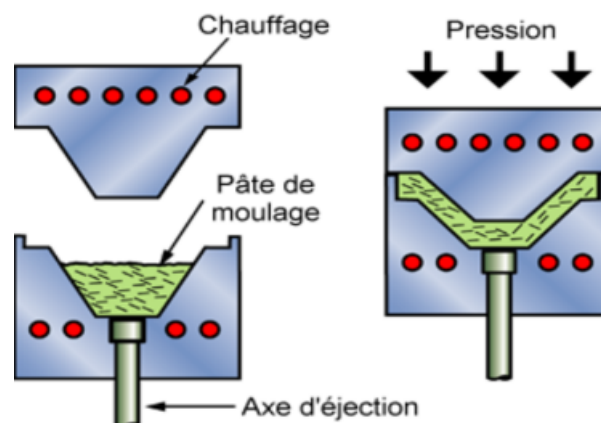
Principe du moulage par compression à chaud de résine.
